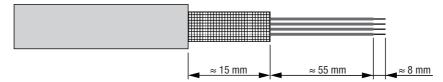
Confección del cable para el módulo de bornes MK 308
